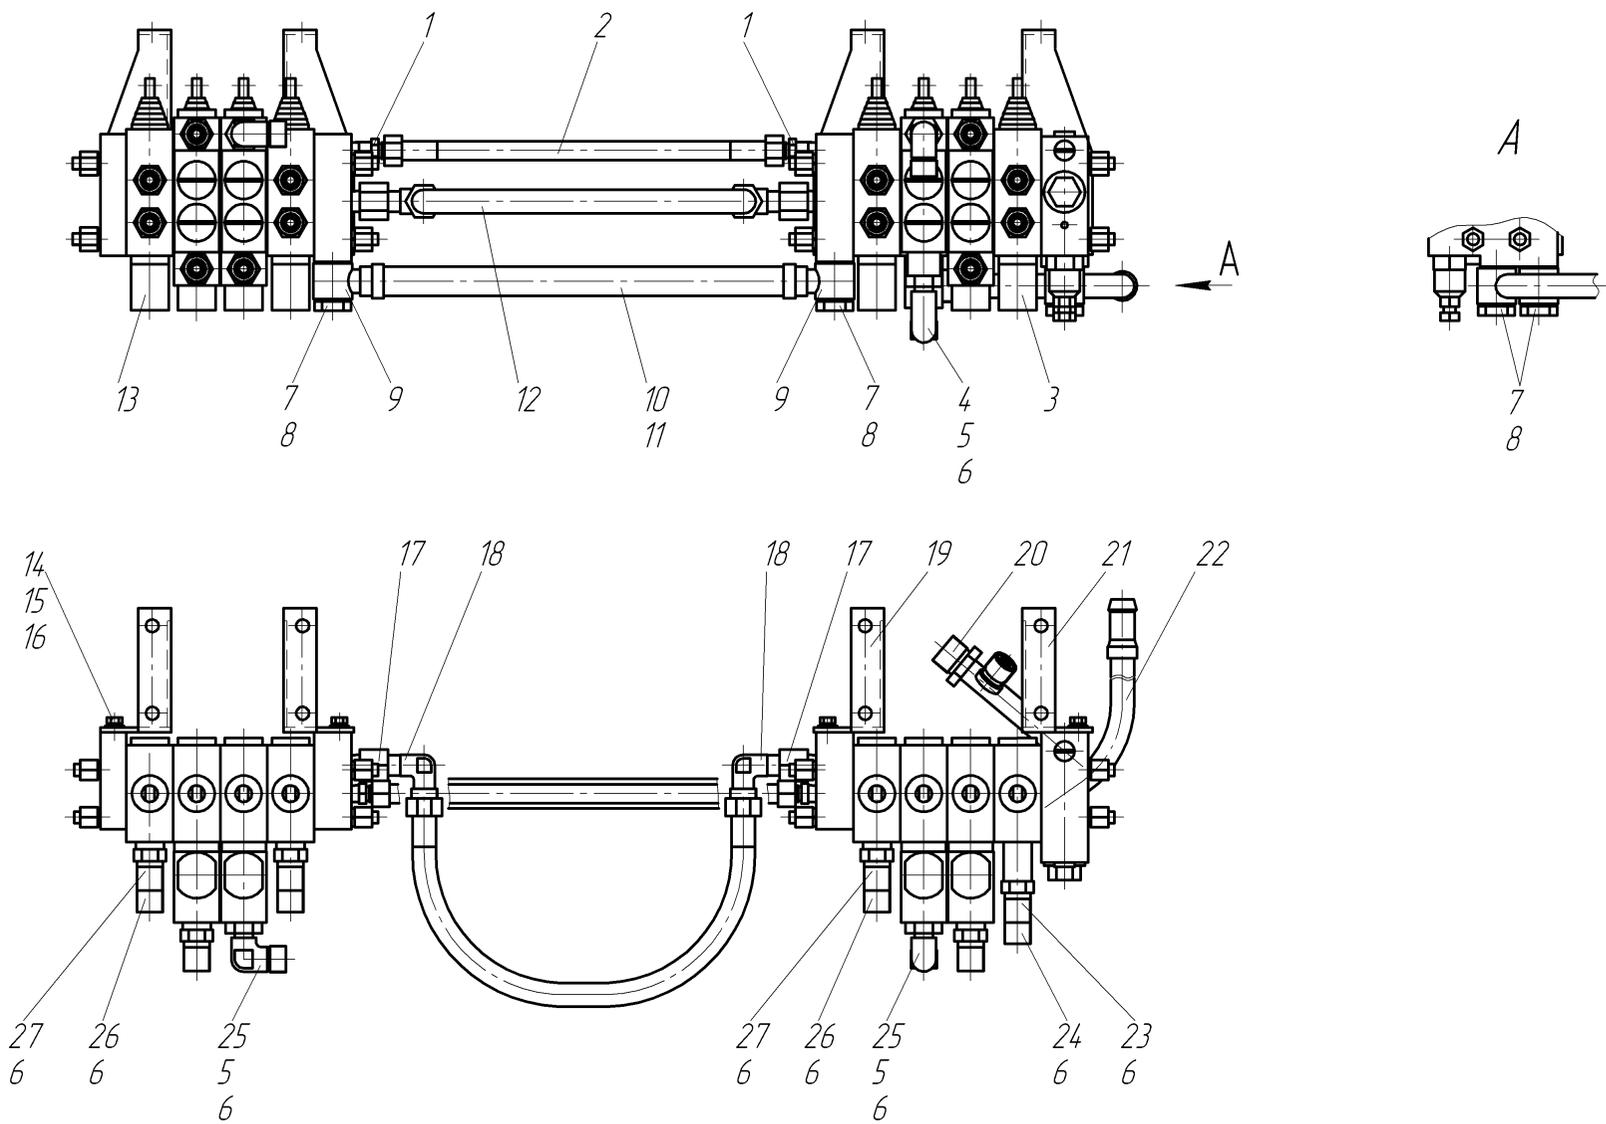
Установка гидрораспределителя 273.05.02.00.000
